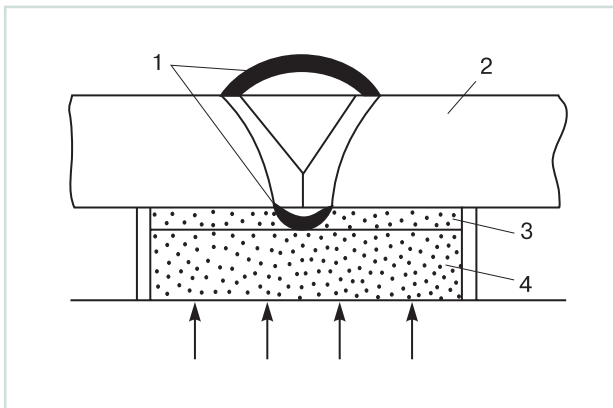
Схема односторонней сварки на двухслойной флюсовой подушке: 1 — усиление лицевой и обратной стороны шва; 2 — свариваемый металл; 3 — верхний, формирующий слой флюса; 4 — огнеупорный слой
